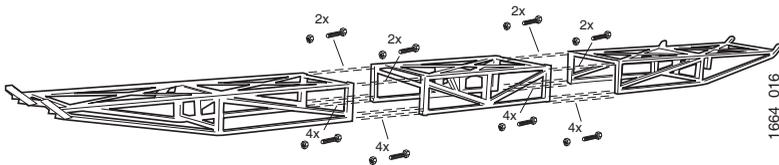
Poutre Y12 + M6 + Y12, assemblage
